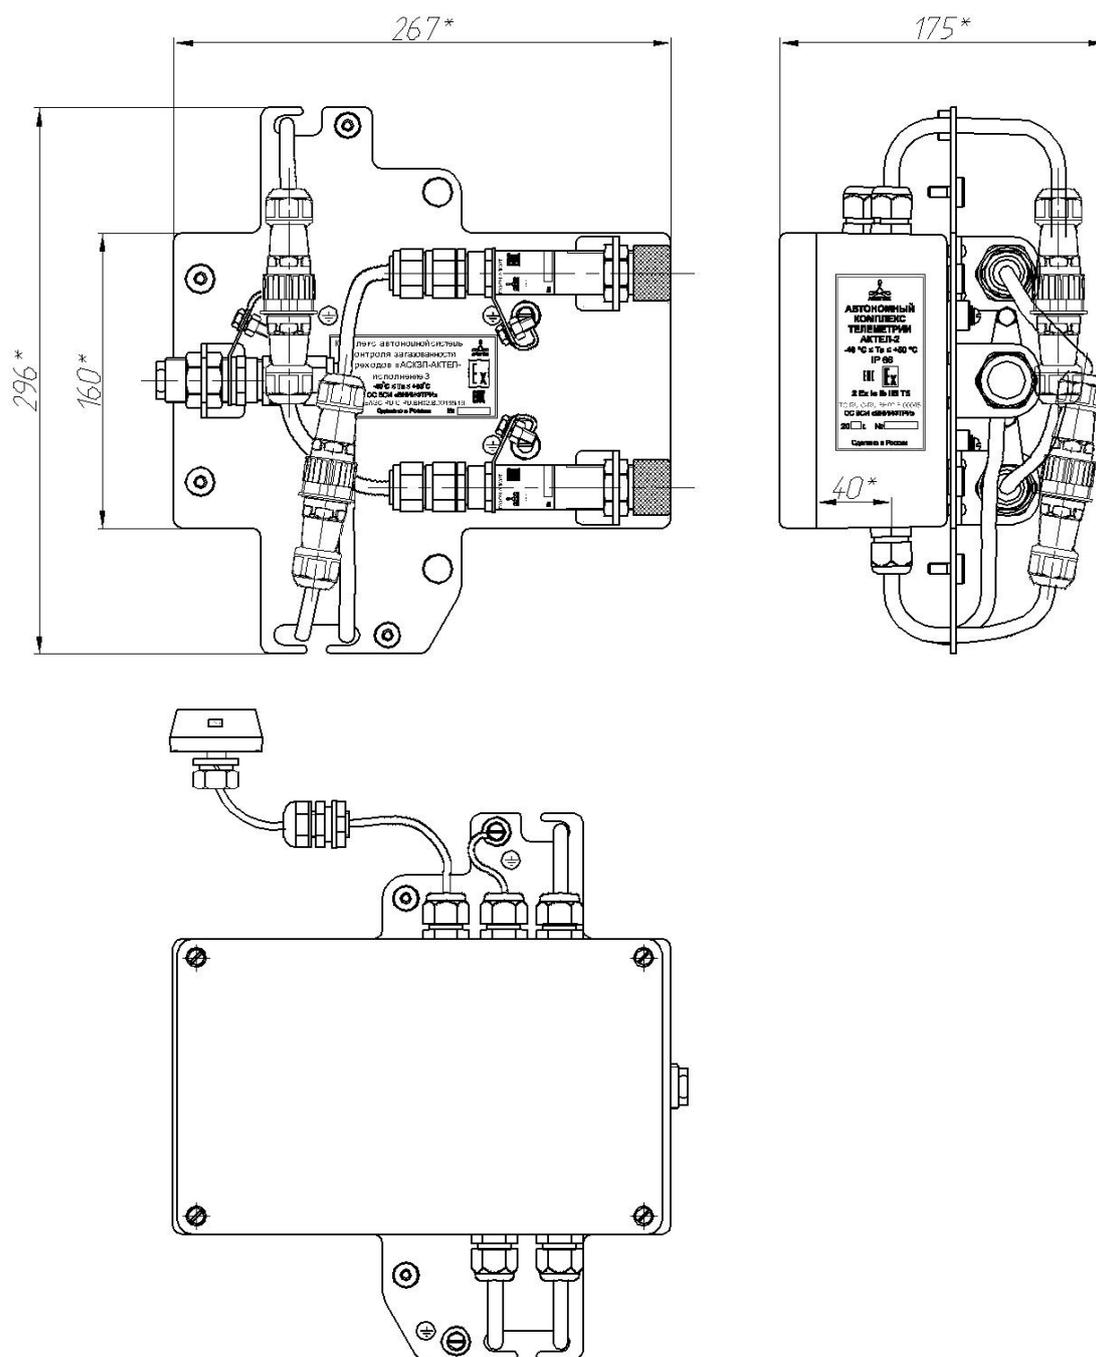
Внешний вид и габаритные размеры комплекса «АСКЗП-АКТЕЛ» исполнение 3 для размещения в корпусе вариант 2
